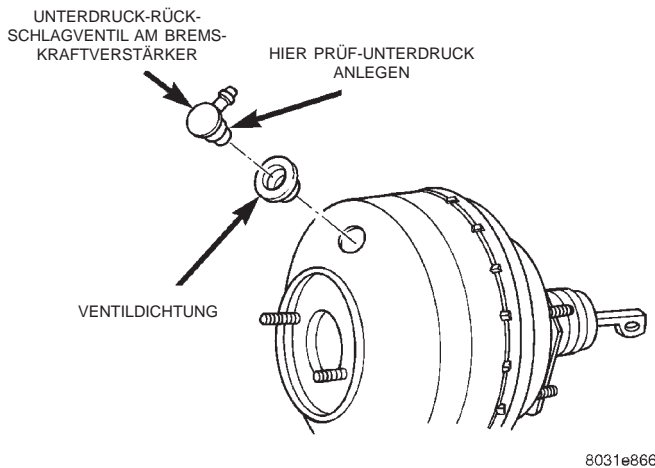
Unterdruck-Rückschlagventil und Dichtung KOMBIVENTIL
